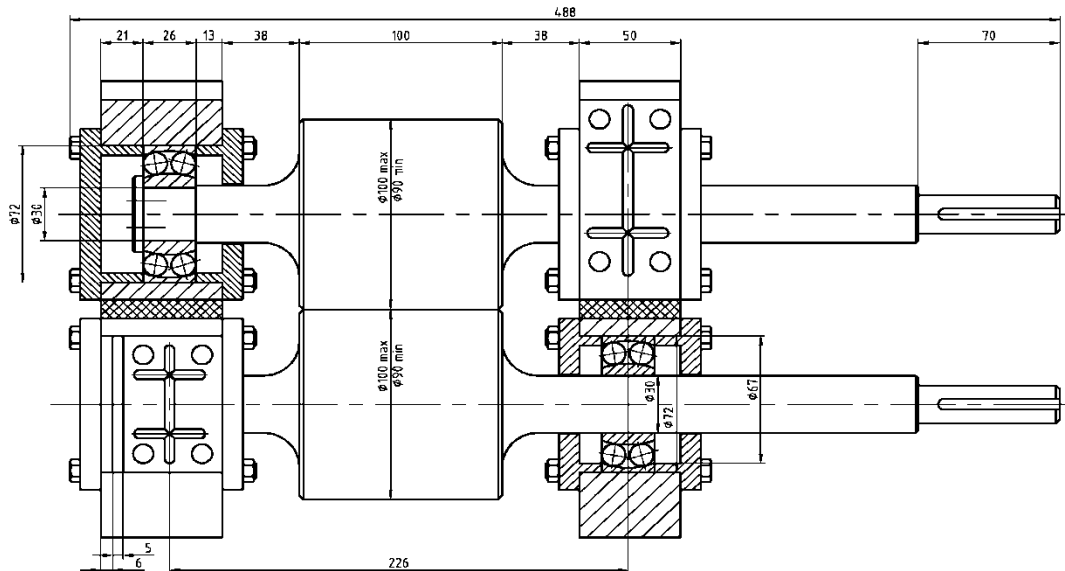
Конструкція вузла робочих валків лабораторного прокатного міні-стану 260x260
